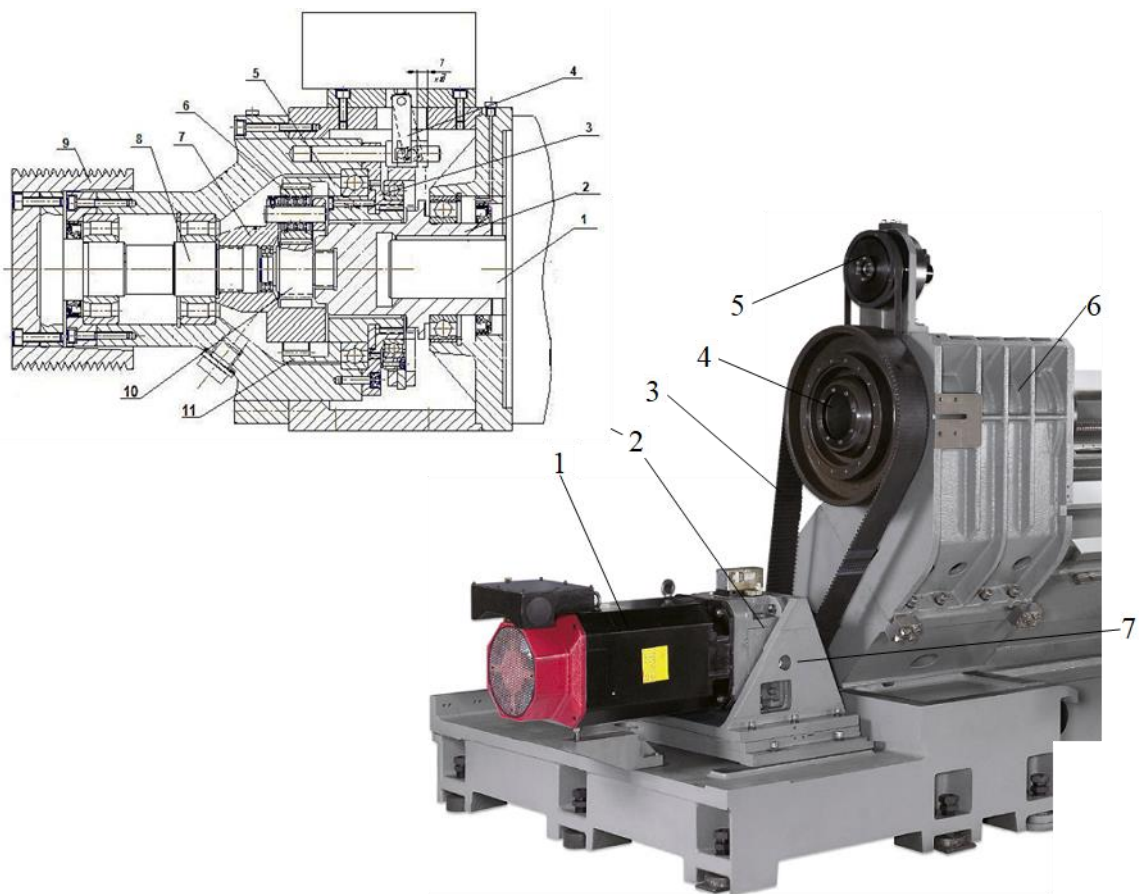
Привід головного руху токарного верстата з ЧПК з планетарною коробкою швидкостей: 1 – привідний двигун; 2 – планетарна коробка швидкостей; 3 – пасова передача; 4 – шпиндель; 5 – вимірювальна система; 6 – шпиндельна бабка; 7 – плита кріплення привідного двигуна з планетарною коробкою швидкостей
